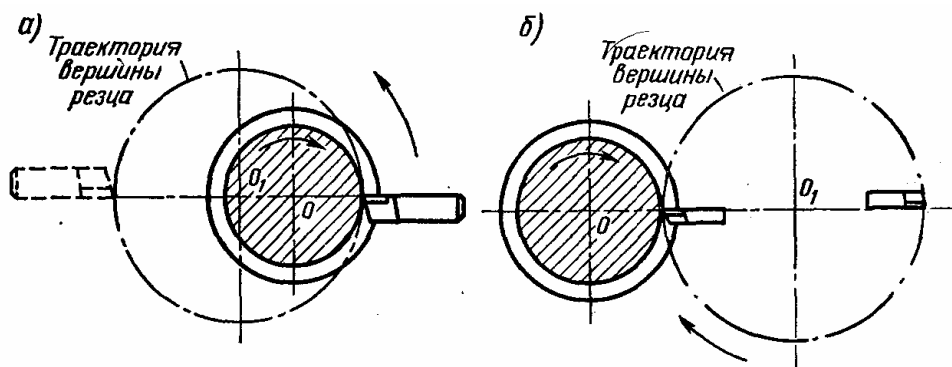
Схема нарезания резьбы вращающимися резцами
